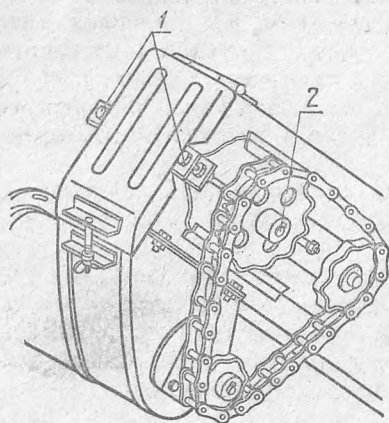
Регулировка натяжения цепей скребковых элеваторов:
